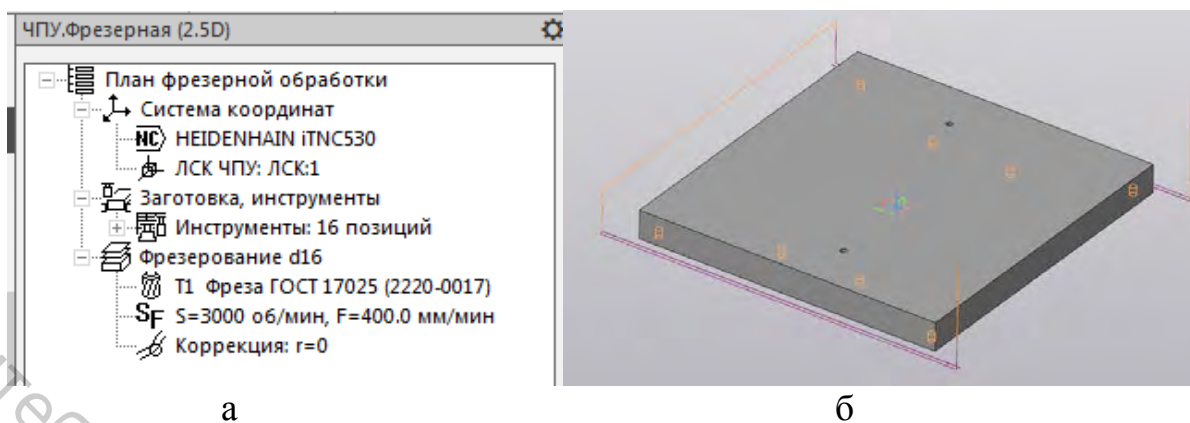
Формирование плана фрезерной обработки:
